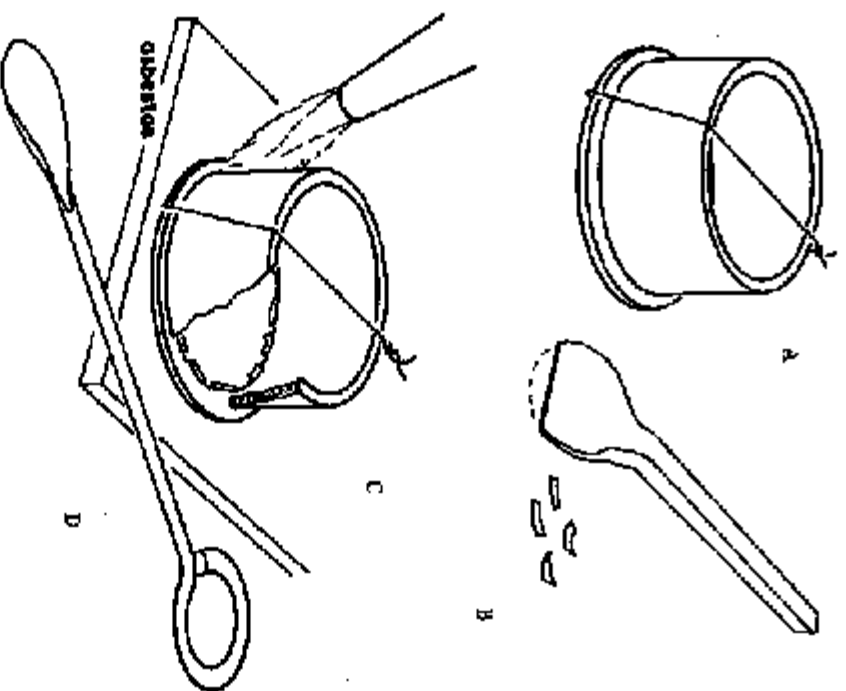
Pueden fundirse unas trocitas de soldadura para que se impregnen en la unión utilizando una flama: (A) amárrase con alambres; (B) aplácase con martillo y córtense los pedacitos; (C) colóquense los trocitos dentro de la pieza, sobre la unión; (D) utilícese una espátula de alambre de hierro.
